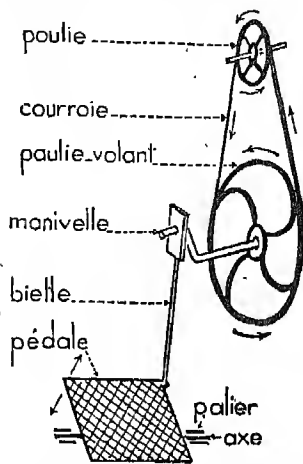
Transmission du mouvement dans une machine à coudre. Décrivez ce mécanisme et expliquez son fonctionnement.
